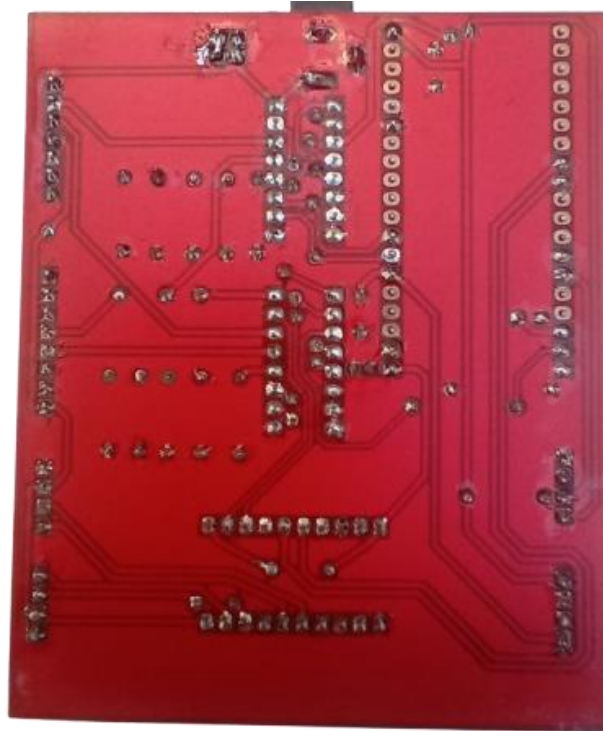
Diseño PCB – Placa finalizada BOTTOM [fuente propia]
